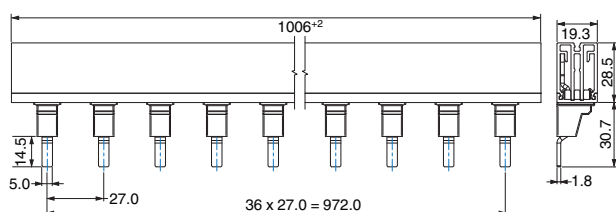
Dimensions de TMC 8...B1...CA (mm)
